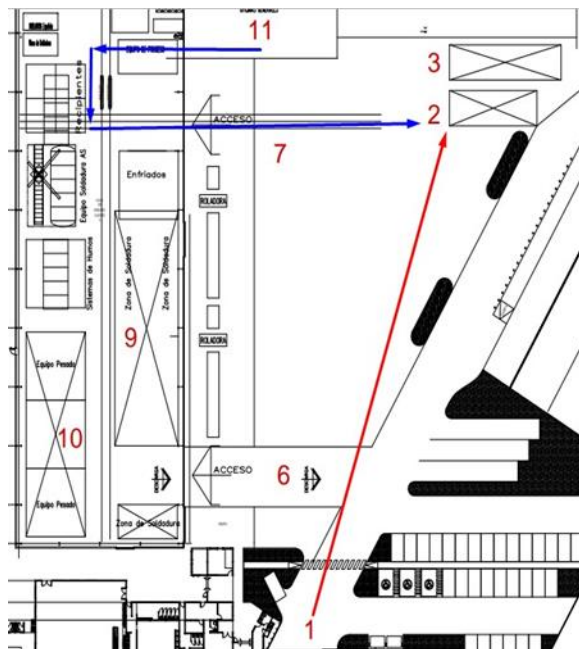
Layout mejorado 1 de la Planta Durosa Santa Rosa SA de CV.
